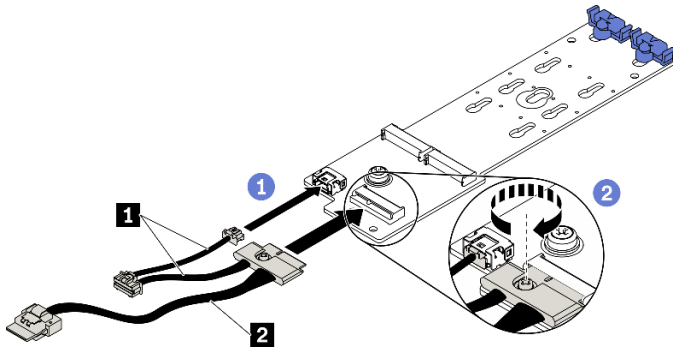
Conexión de los cables de la placa posterior de M.2 a la placa posterior de M.2
